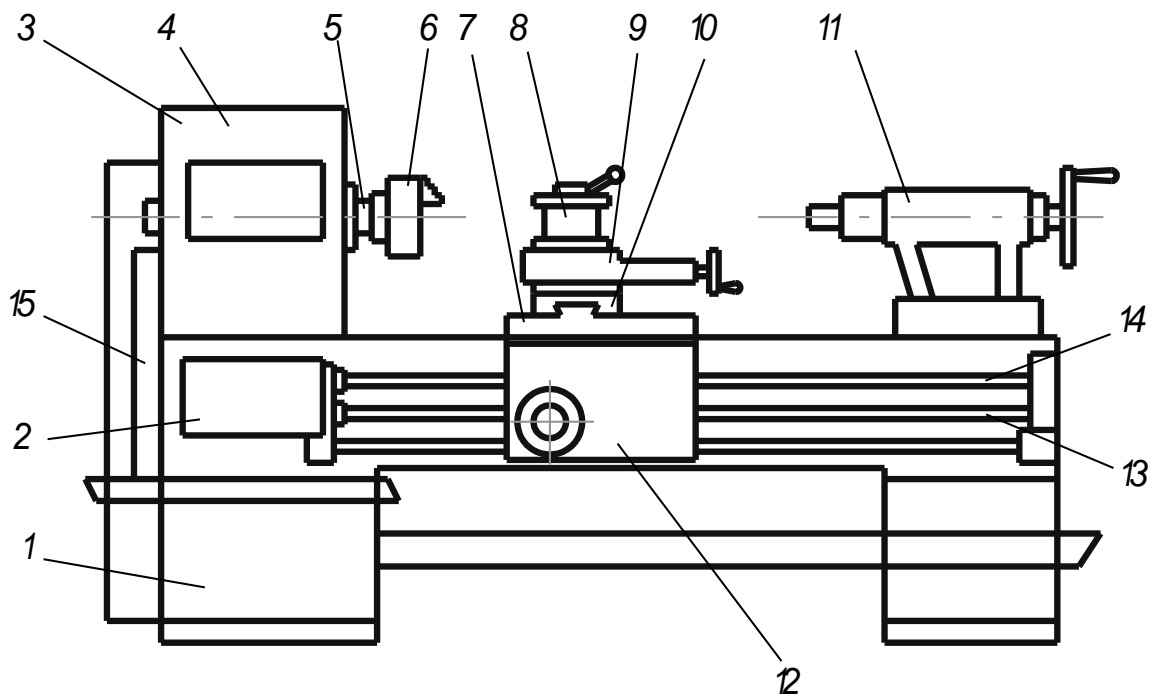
Загальний вигляд токарно-гвинторізного верстата
